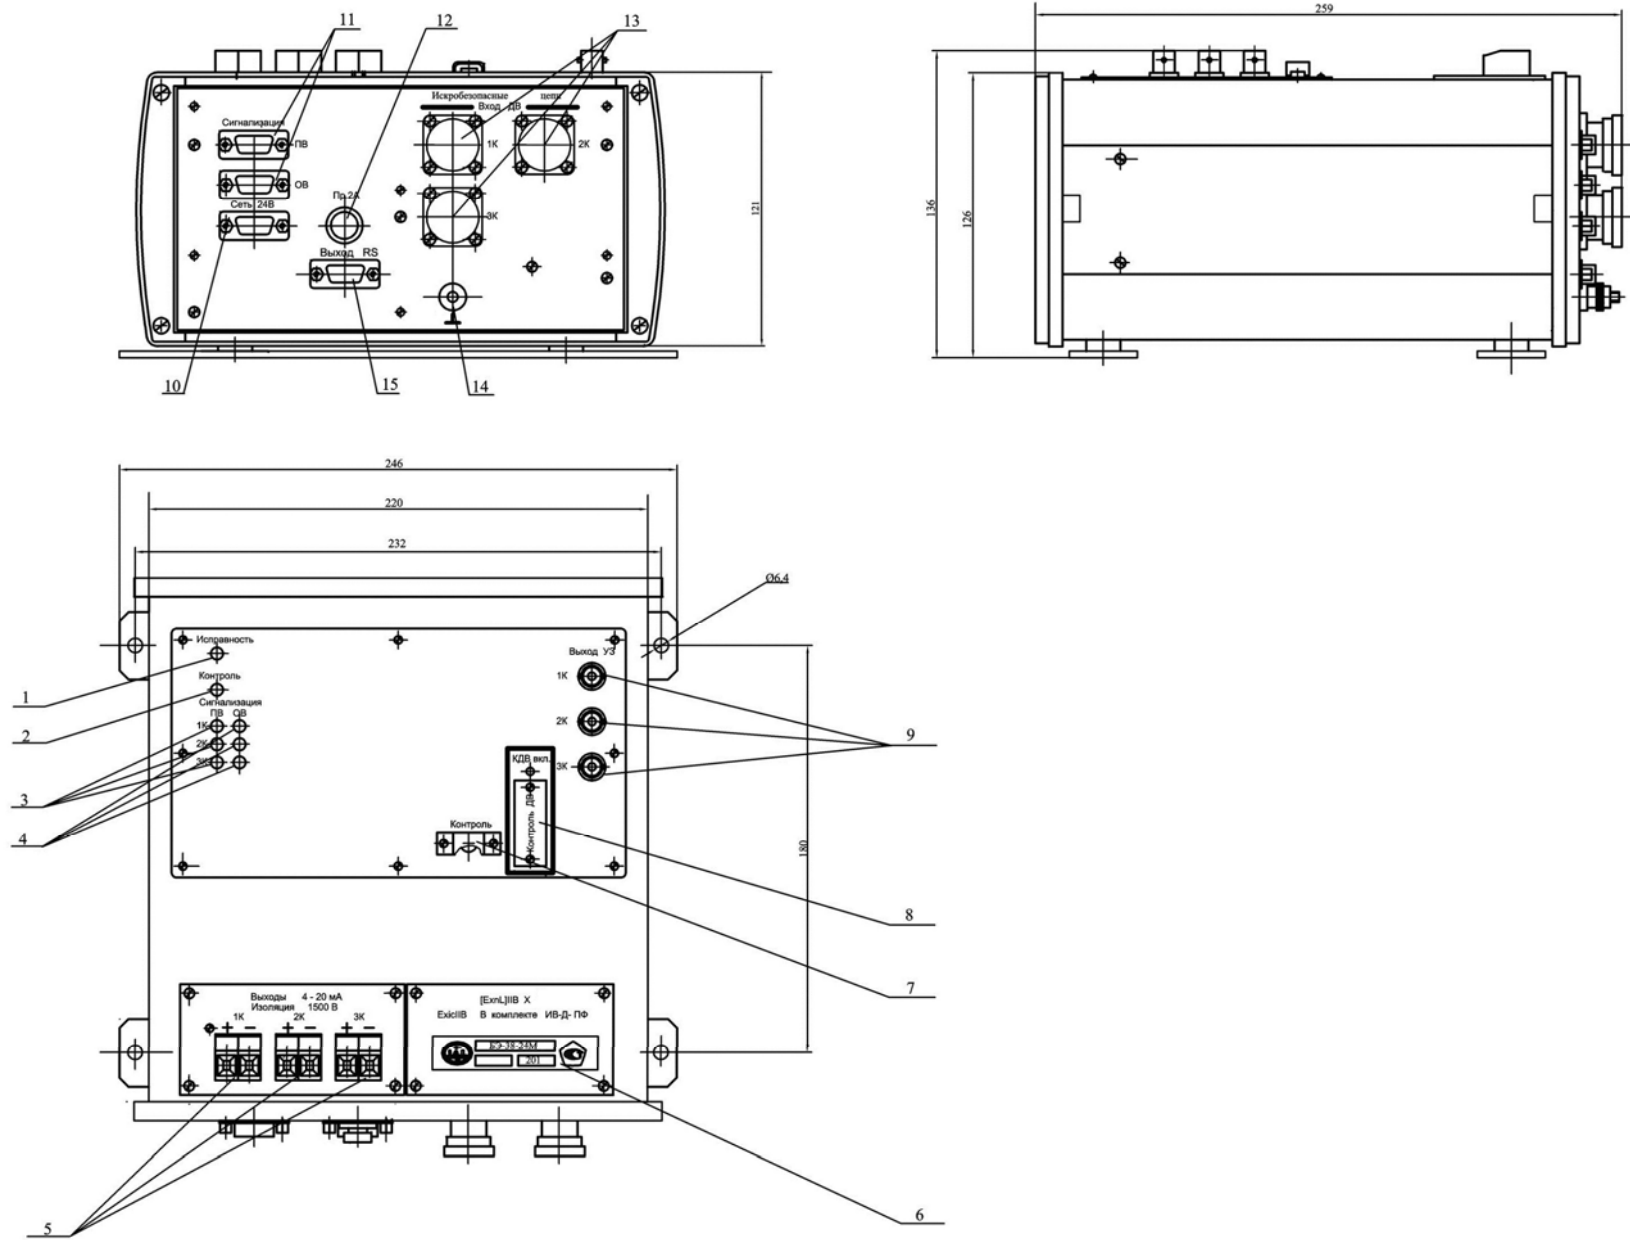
(1 из 2) - Габаритно-установочные размеры блока БЭ-38-24М
